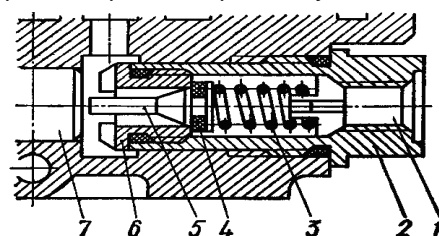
Запірний клапан секції підняття жатки комбайнів «Нива» і «Енисей-1200»: 1 — під'єднувальний отвір; 2 — корпус клапана; 3 — пружина; 4 — гумове кільце; 5 — шток; 6 — гніздо; 7 — поршень
